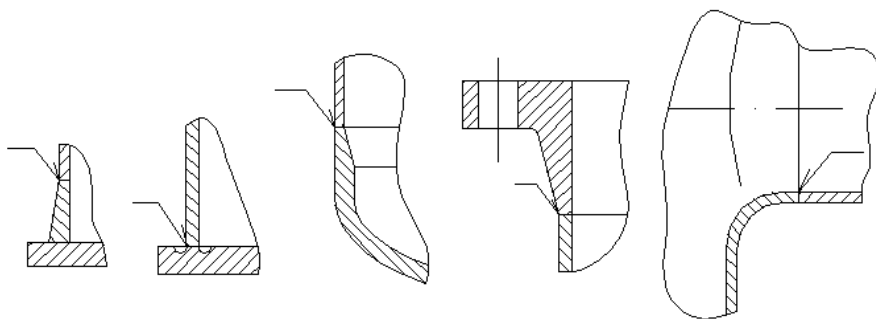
Сварные соединения элементов корпуса
